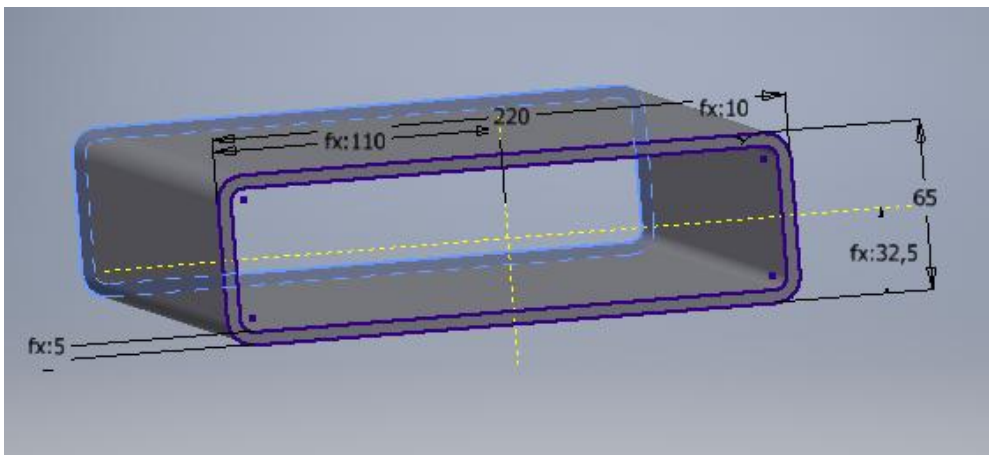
Viga donde se encuentran los puntos de apoyo de la plataforma (vista frontal). Fuente: elaboración propia
